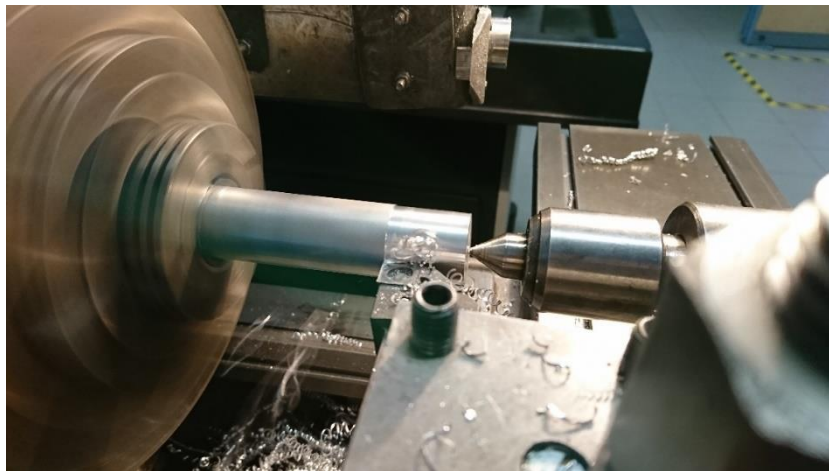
Maquinagem exterior do provete com buril de pastilhas .
